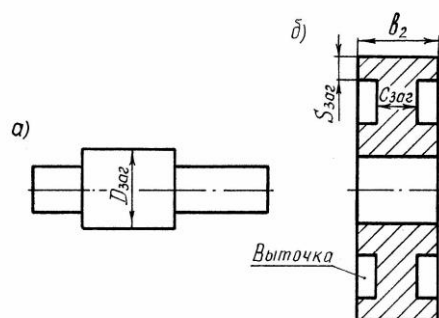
Заготовки цилиндрических зубчатых колес:
